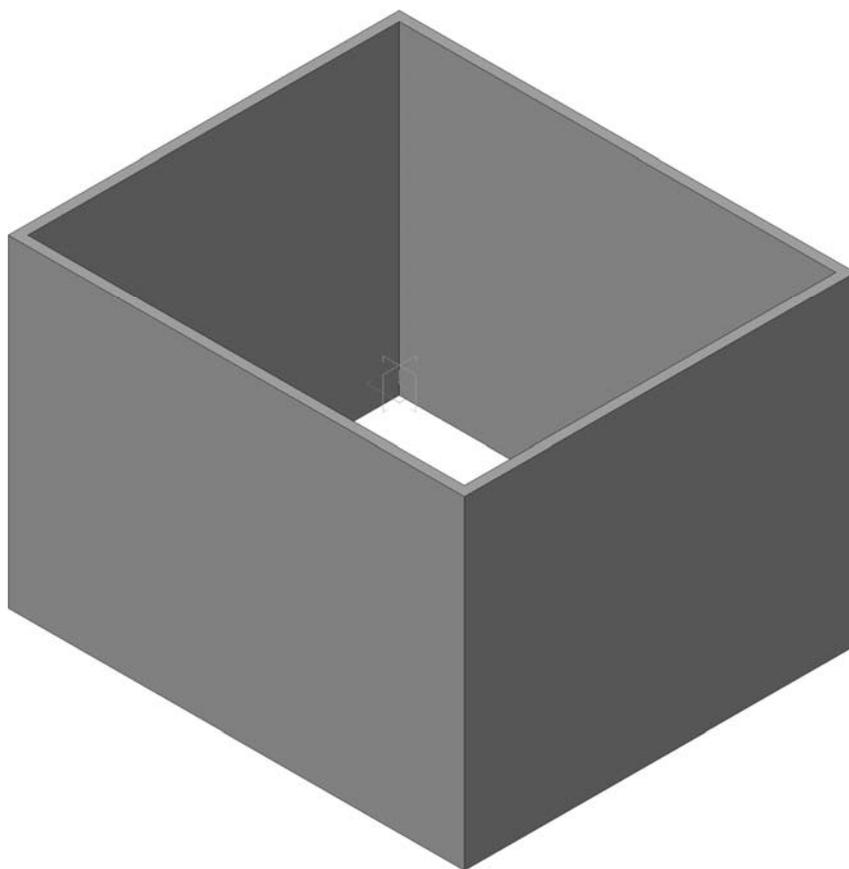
Модель корпуса коробки со стенками равной толщины
